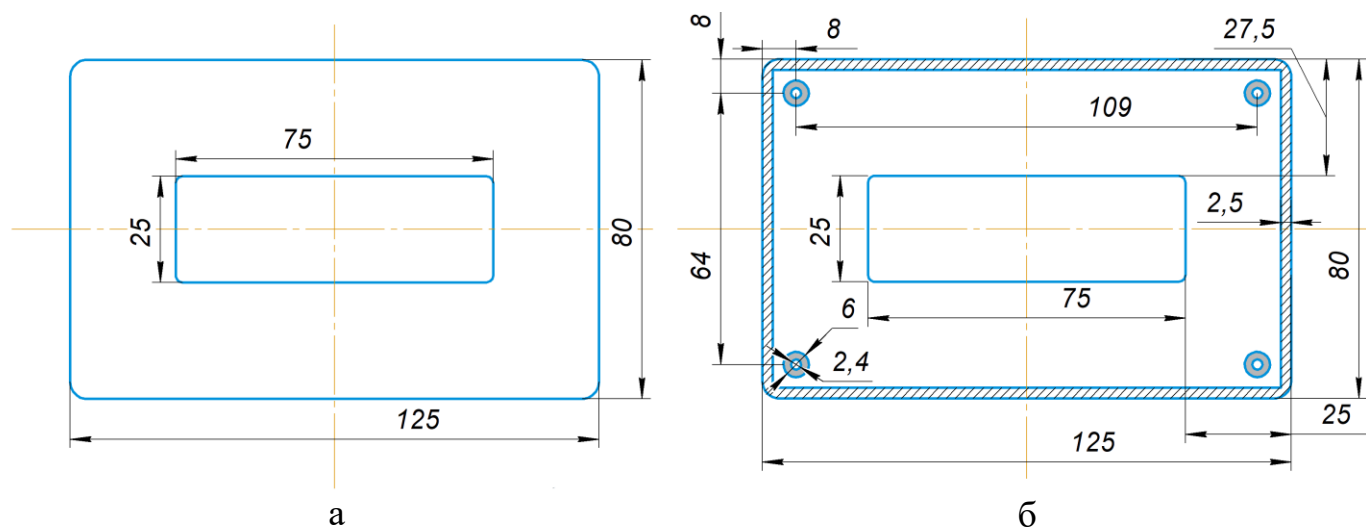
Верхня половина корпусу (лицьова) вид ззовні (а), вид з середини (б)
